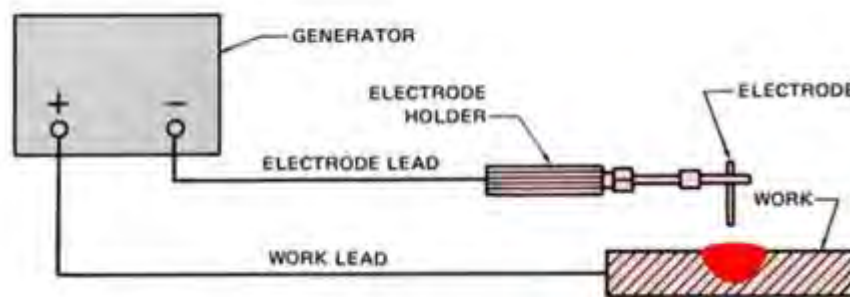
3 Shielded Metal Arc Welding (SMAW)
